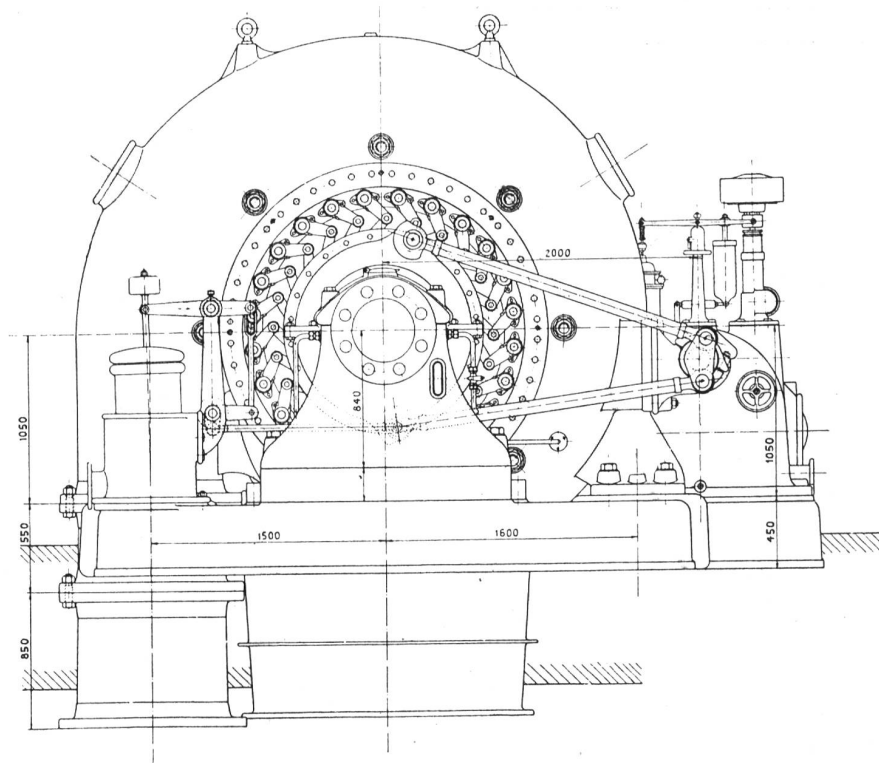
und 6. Längsschnitt und Grundriss einer Generator-Turbine. Maßstab 1 : 45.
